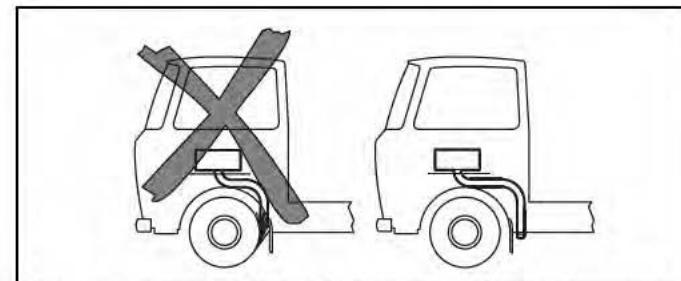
Eviter toute obstruction provoquée par un encrassement
